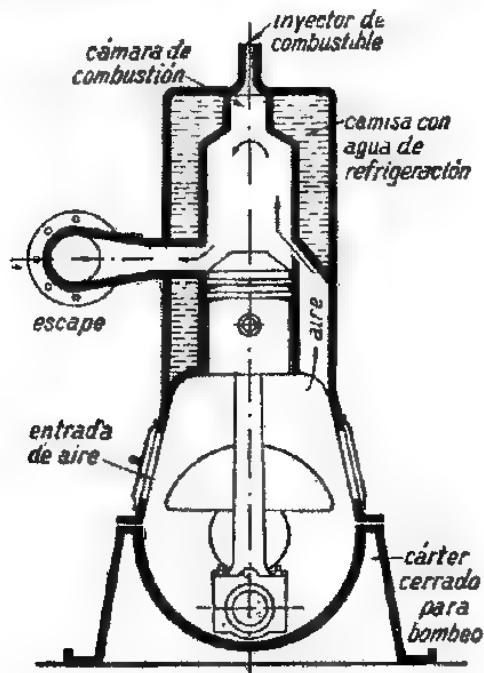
Corte de un motor Diesel de dos tiempos.
